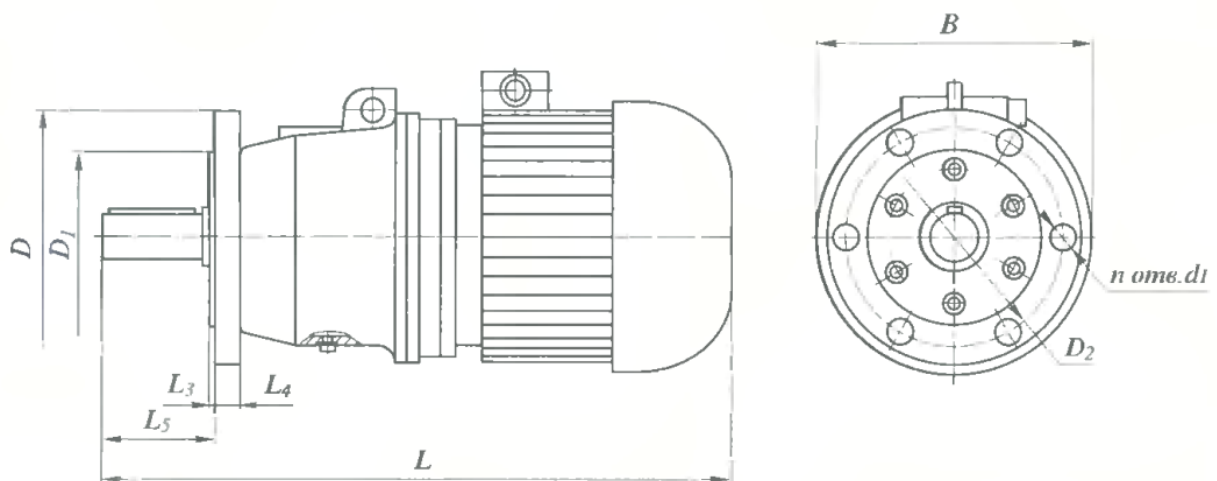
Мотор-редуктор марки ЗМП-50
